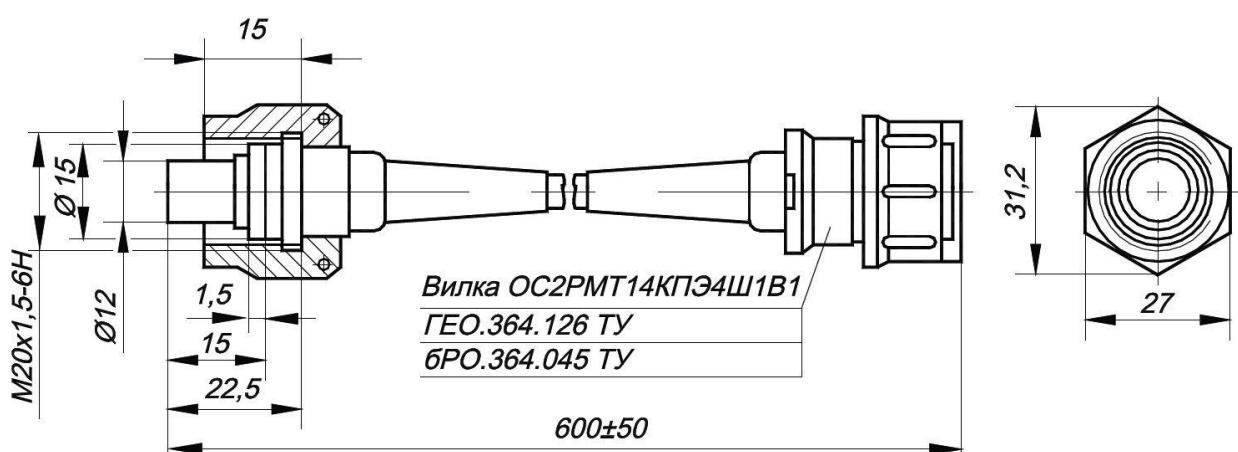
Габаритно-установочные размеры датчика LX-611AM
